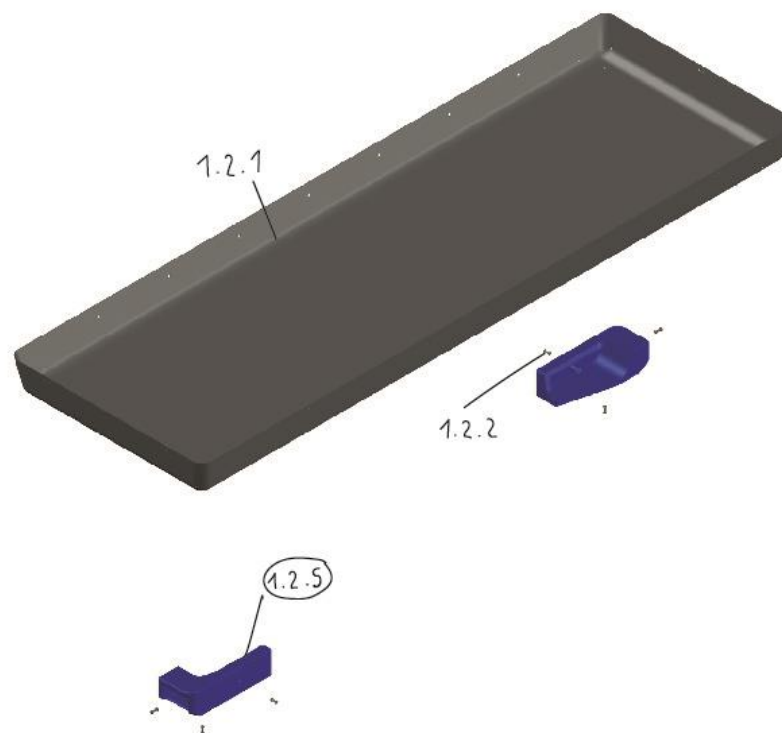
Explosionado de relaciones pieza 1.2.5
